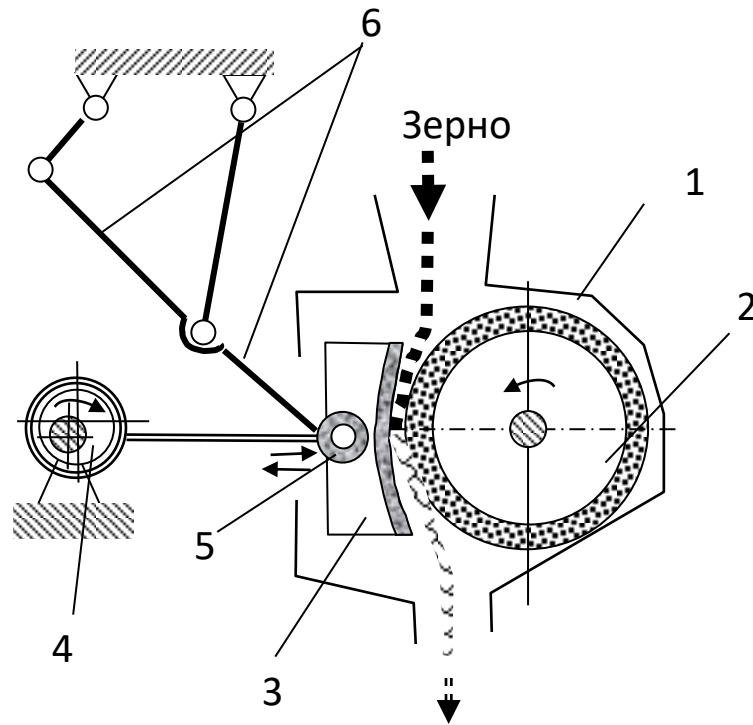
Схема верстата з вібродекою: 1 – корпус; 3 – дека; 2 – валок; 5 – пружний шарнір; 4 – ексцентриковий механізм; 6 – напрямний
